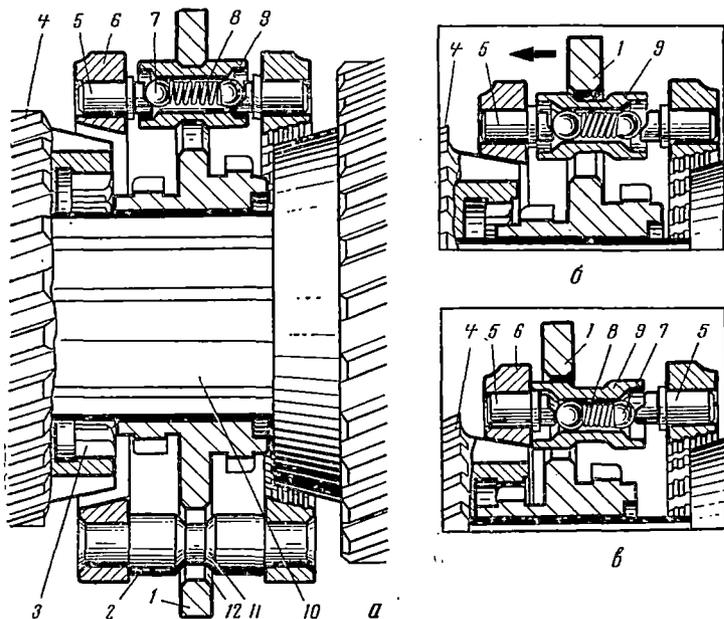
Устройство и схема работы синхронизатора коробки передач автомобиля ЗИЛ-164А (ЗИЛ-130):
